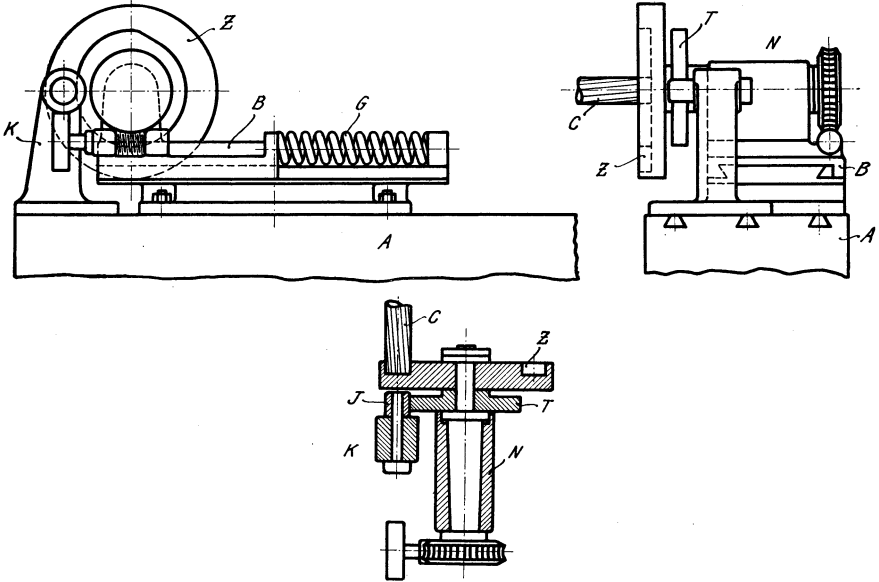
Die Kopiervorrichtung für Wagrechtfräsmaschinen.
